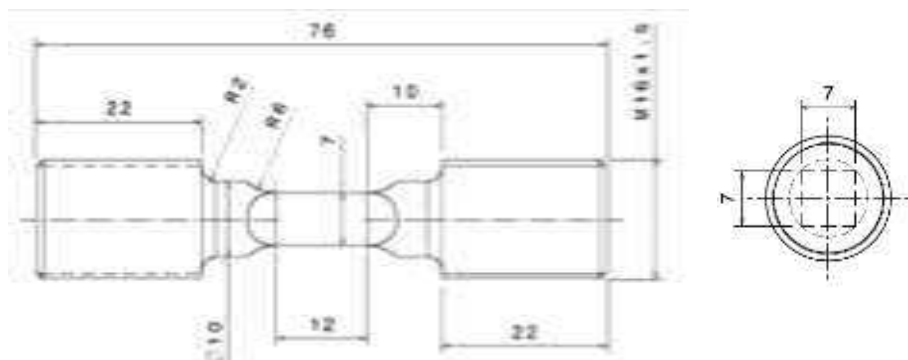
Schéma des éprouvettes à section carrée utilisées pour la fatigue interrompue.
